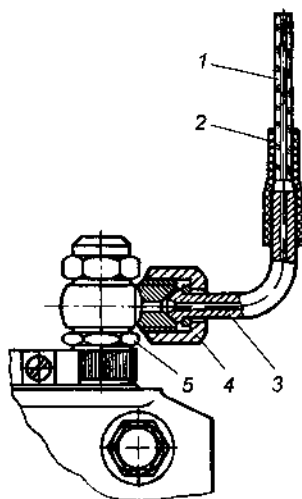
Установка моментоскопа на топливный насос: 1 — стеклянная трубка; 2 — соединительная трубка; 3 — отрезок трубки высокого давления; 4 — накидная гайка; 5 — штуцер
